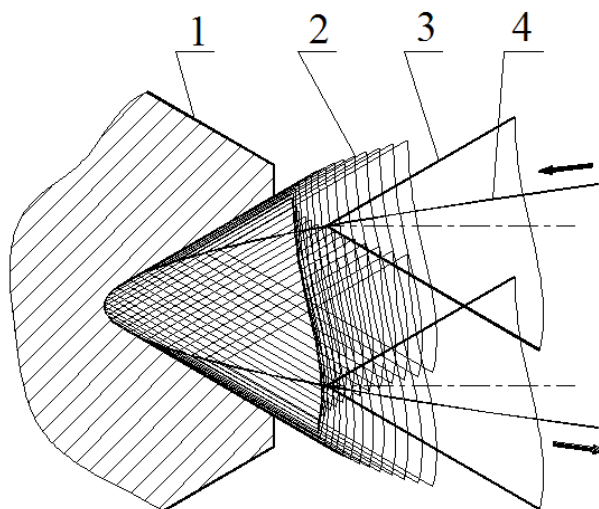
Процесс формирования профиля нарезаемой резьбы зубом резбообразующей части инструмента
